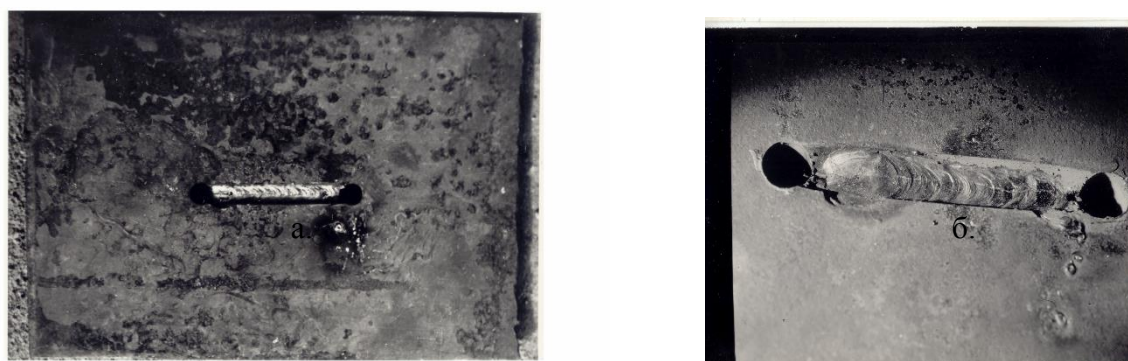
Внешний вид проб Теккен: а. Вид сверху всей пластины; б. Вид шва.
